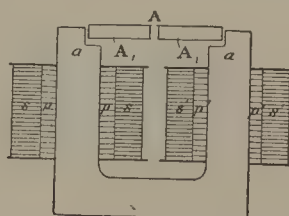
Coupe du transformateur de haute tension de M. Klingelfuss.
